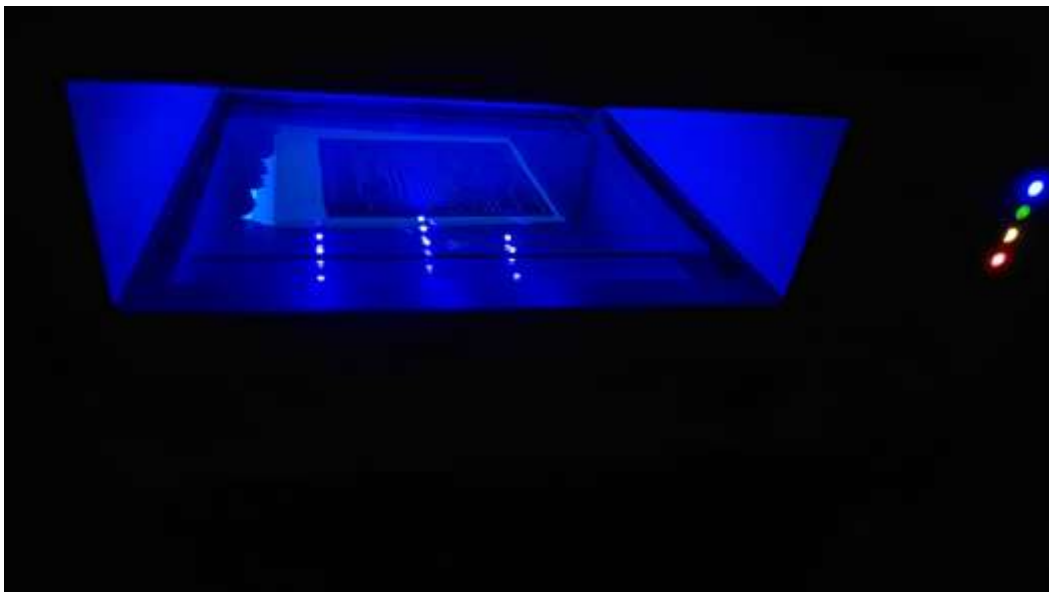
PCB com a máscara e a camada de dry film sendo exposta a luz violeta
